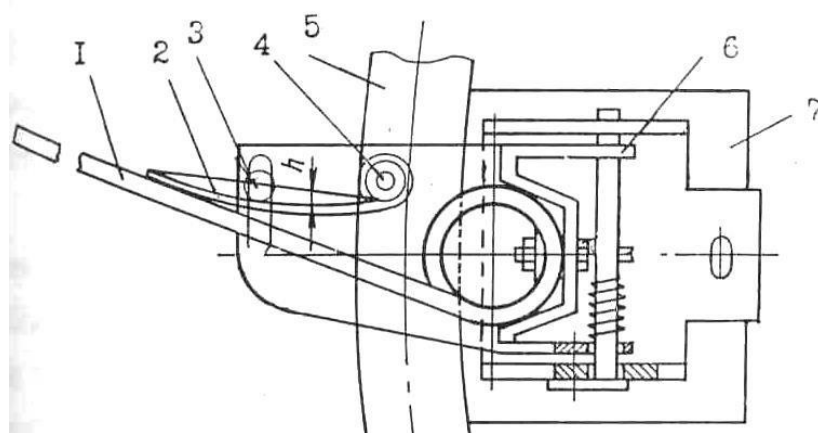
Схема удосконалення робочих органів ротаційних граблів – ворушилки: 1 – пружинні зуби; 2 – вітровий щит; 3 – упор; 4 – шарнір; 5 – обід ротора; 6 – поворотна обойма; 7 – кронштейн
